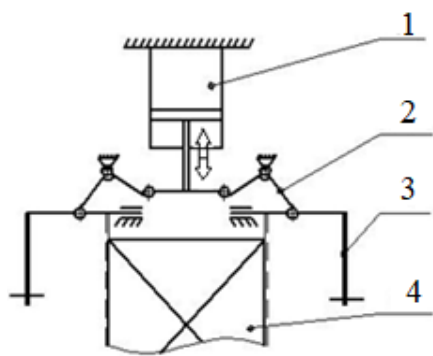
Схема захоплювального пристрою важільного типу зі зворотно-поступальним рухом стулок: 1- пневмопривод; 2 - важелі; 3 - стулки; 4 - упаковка
